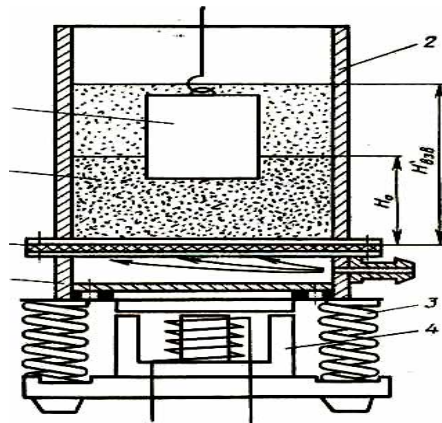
Схема вібровихрового відновлення деталей полімерними матеріалами: 1 – деталь; 2 – ванна; 3 – пружина; 4 – вібратор; 5 – пневматична камера; 6 – пориста перегородка; 7 – полімерний порошок
